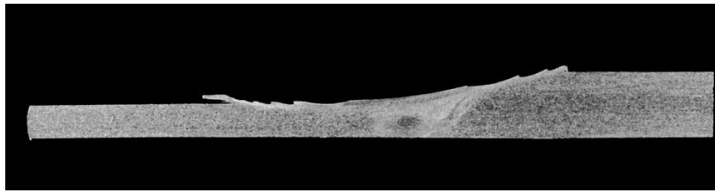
Soldadura a tope de espesores disimiles. 1 mm a 2 mm de la aleación 6111 – T4. (19)
